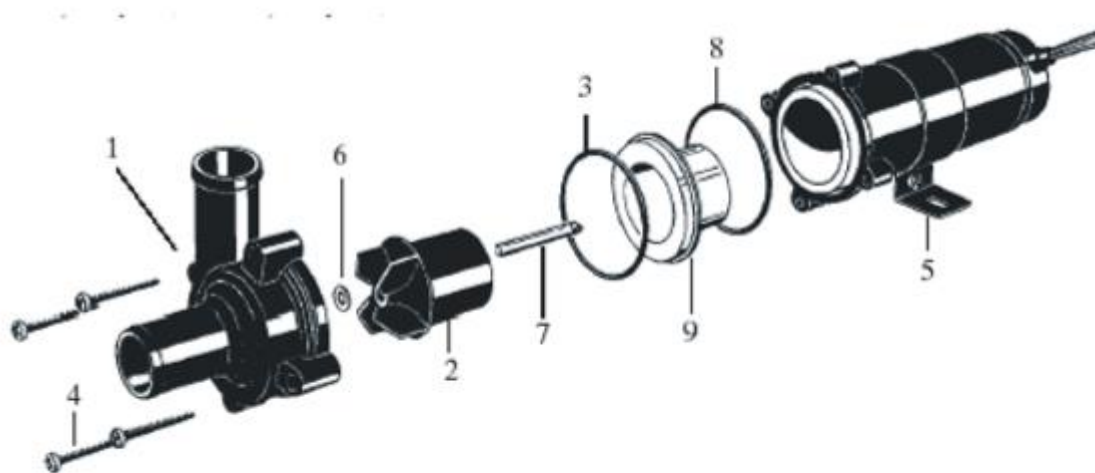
Насосна станція *SPX Johnson Circulating pump 24V*: 1 – корпус; 2 – лопатеве колесо; 3 – кільце; 4 – гвинти; 5 – опора; 6 – шайба; 7 – вал; 8 – ущільнююче кільце; 9 – магнітний корпус;
